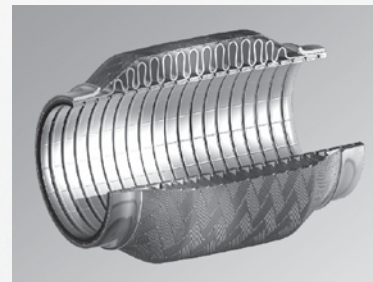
Schnitt durch ein Entkoppelelement für PKW-Abgasanlagen. Es besteht aus einem äußeren Geflecht, einem Metallbalg und einem Agraff-Schlauch zur Strömungsführung.
